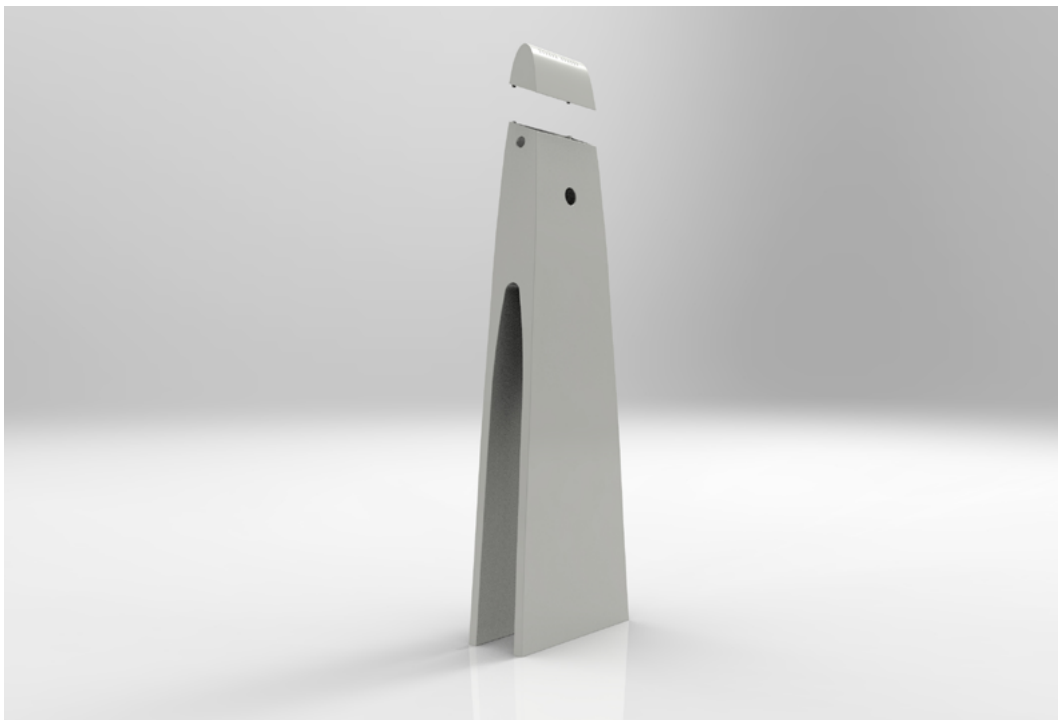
, 104 y 105: detalles de cómo se monta y desmonta la tapa de la parte superior.
